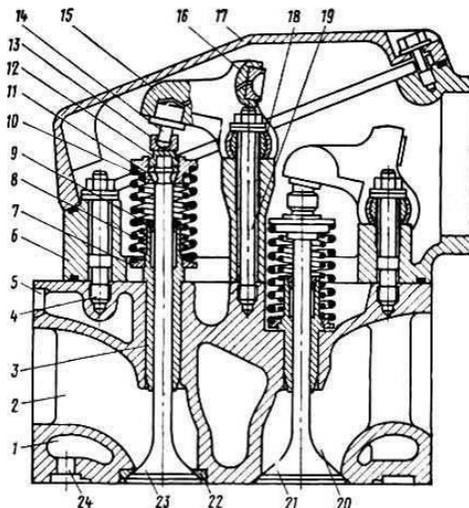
Крышка цилиндра дизеля Д49
